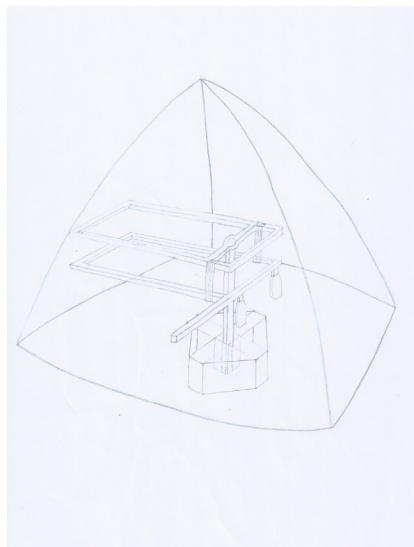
Boceto de la estructura de la boca del monstruo. Sistema de contrapeso.
